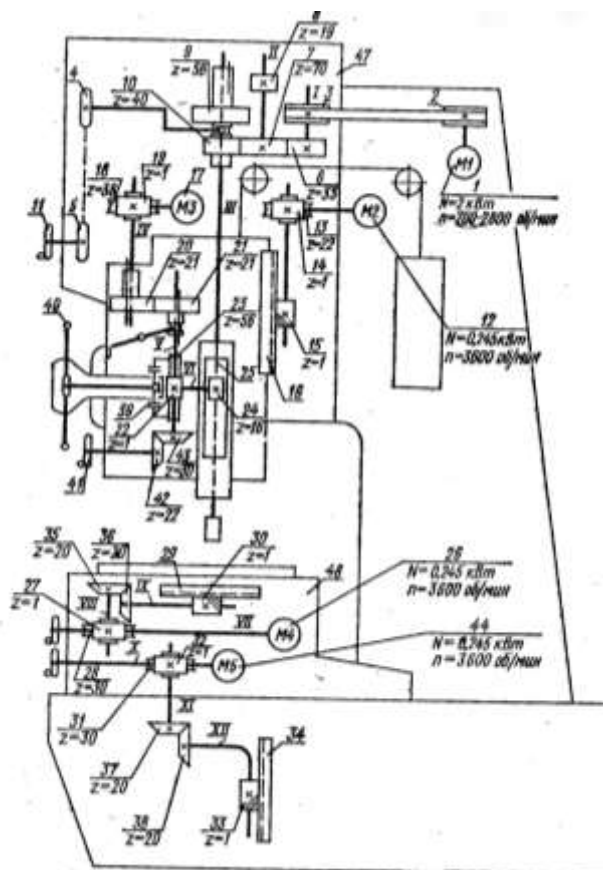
Кинематическая схема станка мод. 2Д450
